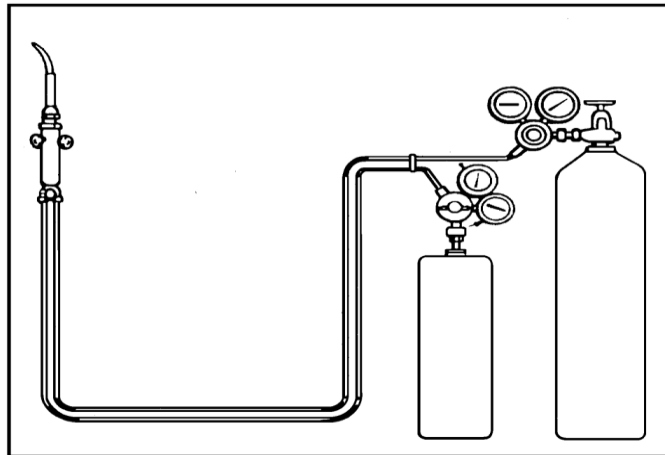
Sistema de soldadura por gas. (OXGASA, 2016).
